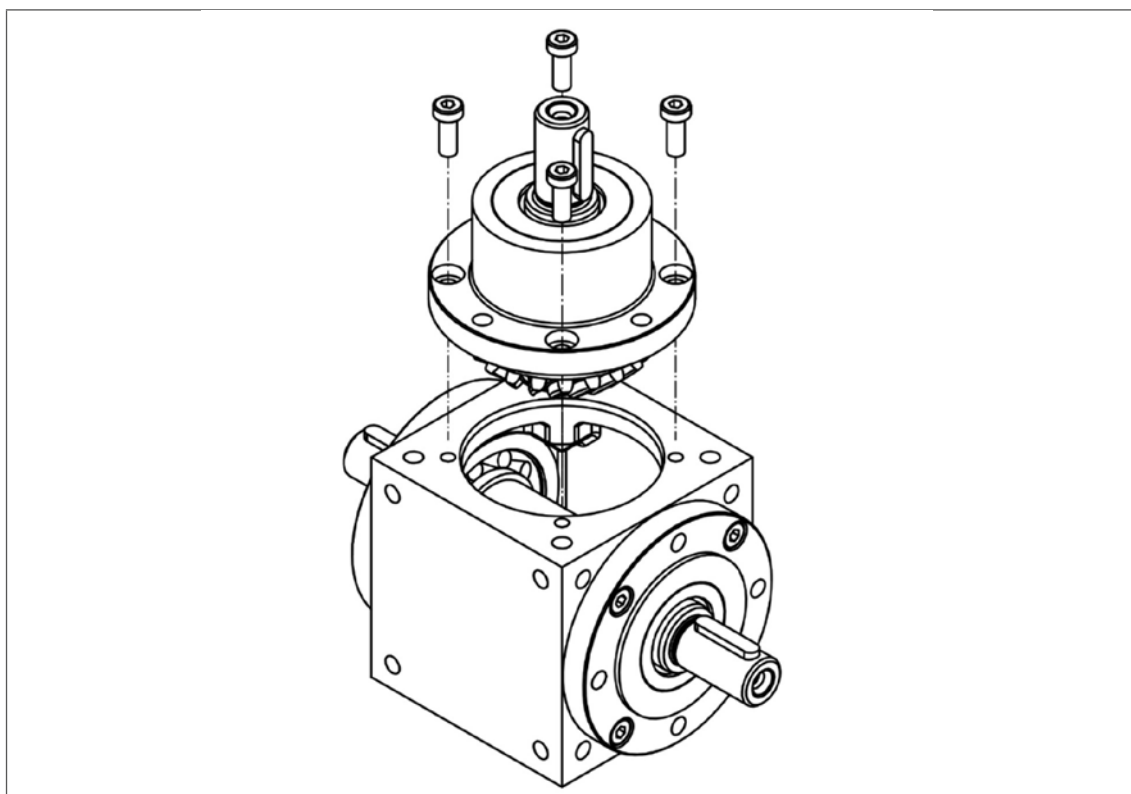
Montaggio / smontaggio della flangia cuscinetto
